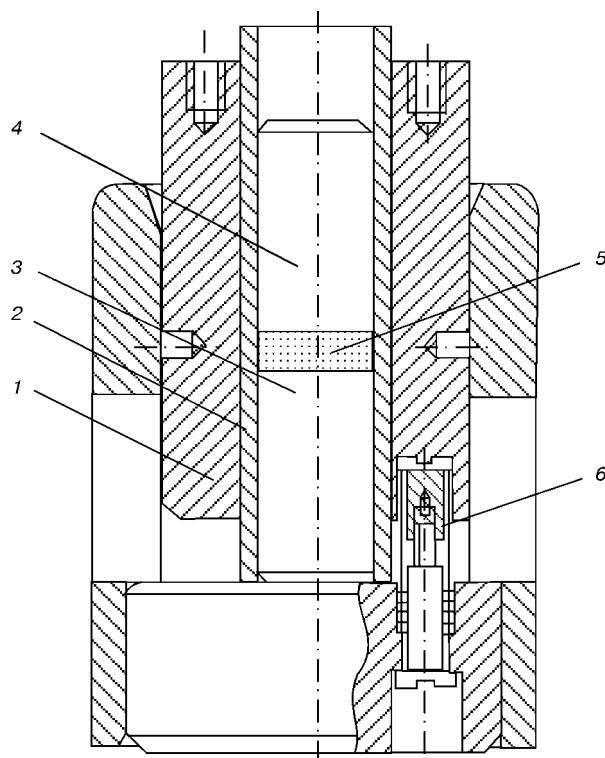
Пресс-форма для изготовления таблеток модификаторов: 1 — обойма; 2 — вкладыш; 3, 4 — соответственно нижний и верхний пуансоны; 5 — таблетка модификатора; 6 — выталкивающее устройство
